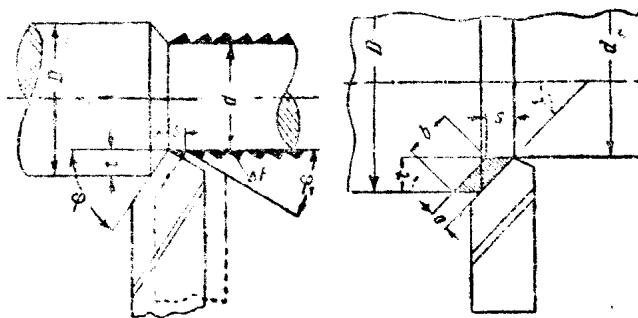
车刀加工后的表面形状 图 8 车刀加工时的几何参数
